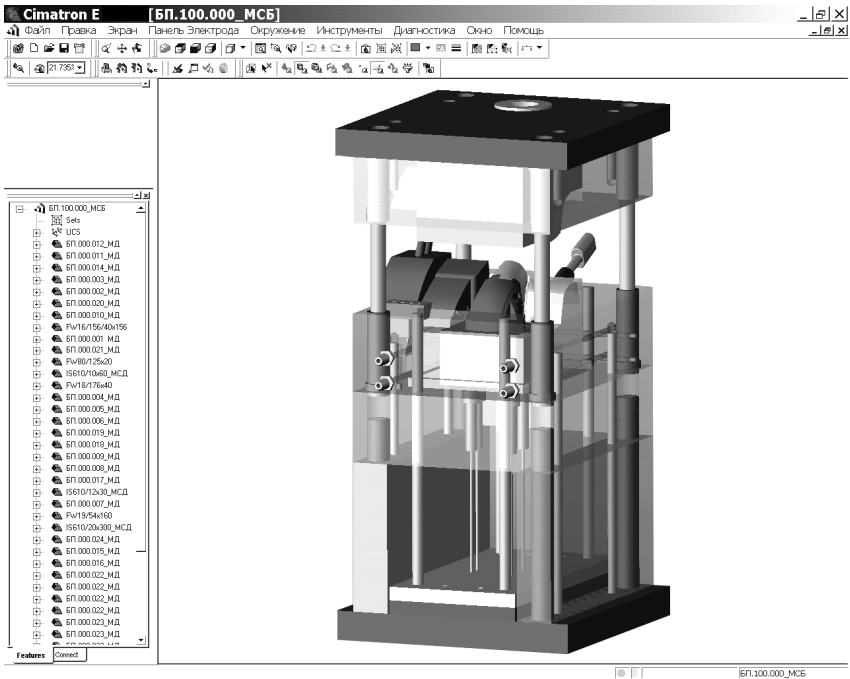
Модель прес-форми в підсистемі MoldDesign
